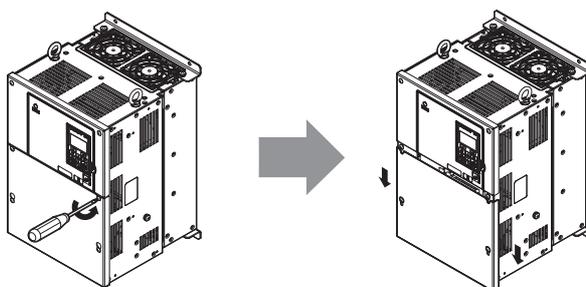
Снятие крышки клеммного блока для ПЧ в корпусе IP00
